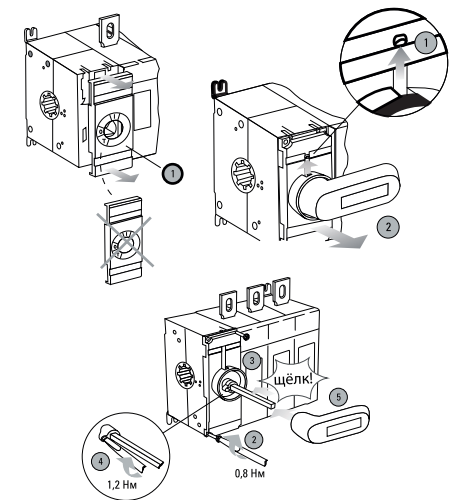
Установка рукоятки управления прямой установки 315-1600А
